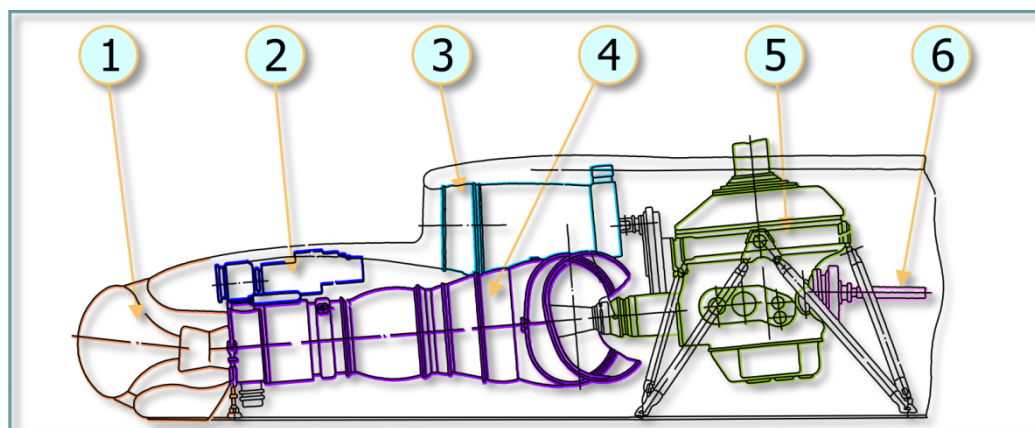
Схема расположения агрегатов силовой установки (вид сбоку):
